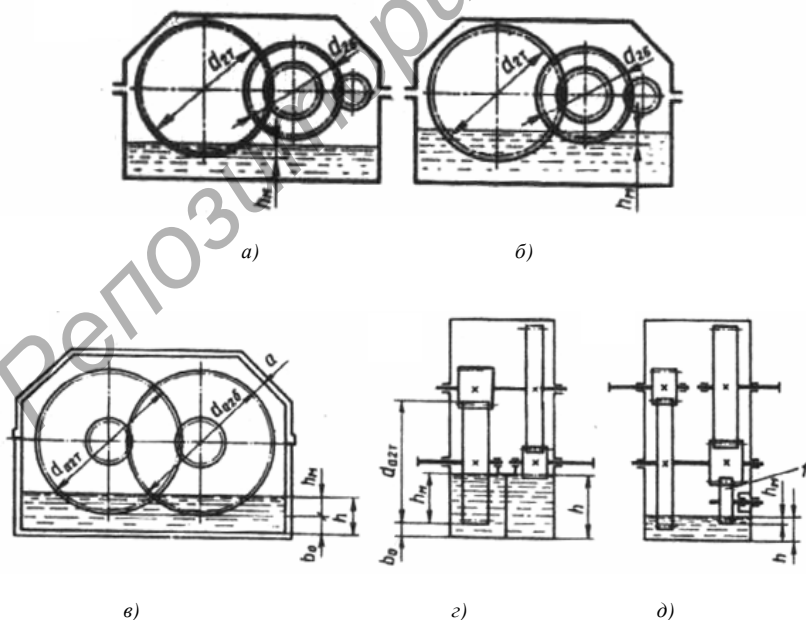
Глубина погружения в масло деталей цилиндрического редуктора
